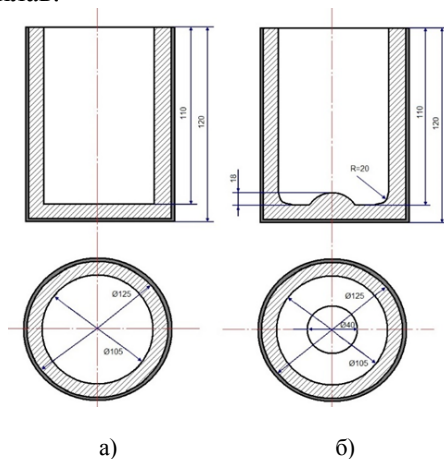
Ескіз конструкції футерівки сталерозливних ковшів: а — традиційної конструкції; б — розробленої конструкції
